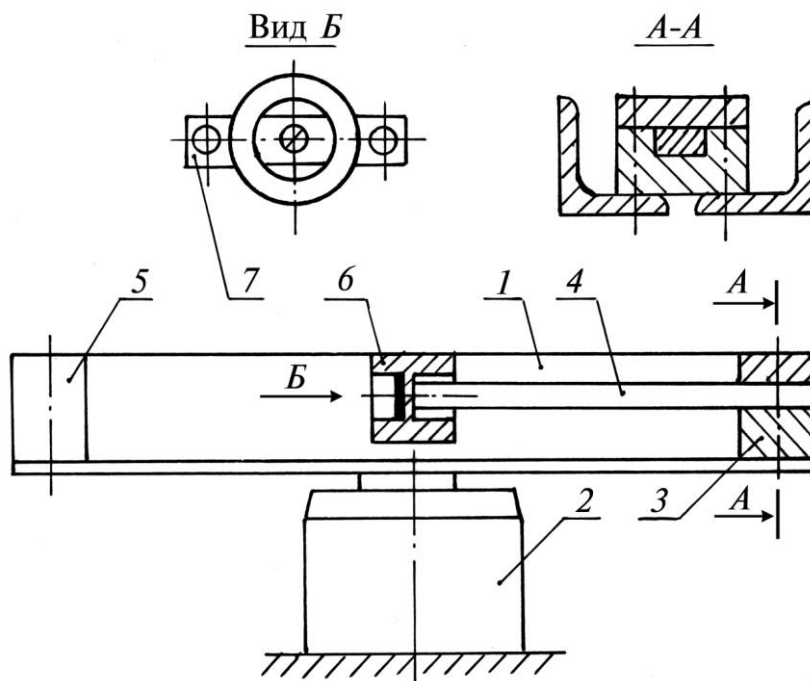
Конструкція пристрою для встановлення зразка на столі вібратора.
